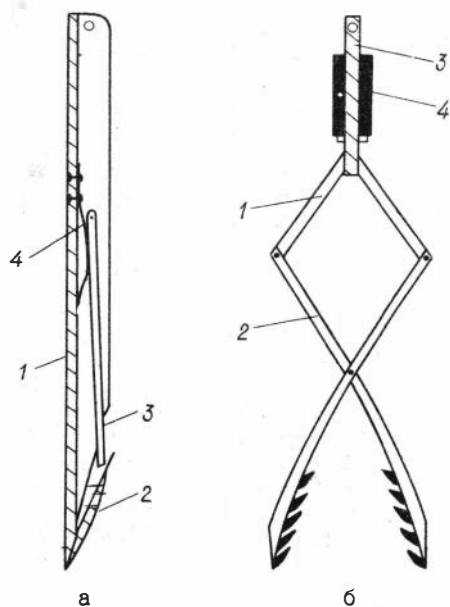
а) Крюкообразный ловильный инструмент: 1-швеллер; 2-крючок; 3-защелка; 4-пружина.
